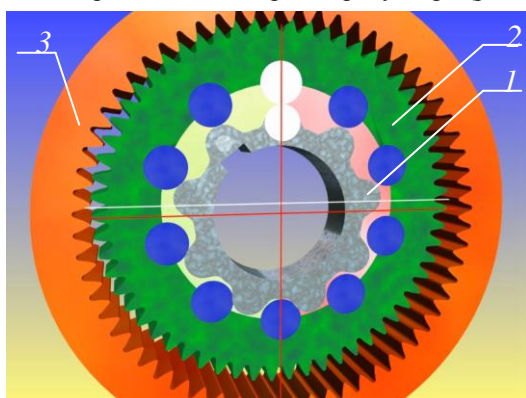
Схема движения вытеснителей в планетарных гидромоторах семейства унифицированных рядов ПРГ-33, ПРГ-22, ПРГ-11, и ПРГ-8: 1 – охватываемый вытеснитель (солнечная шестерня); 2 – охватывающий вытеснитель (сателлит); 3 – корпус (коронная шестерня)
